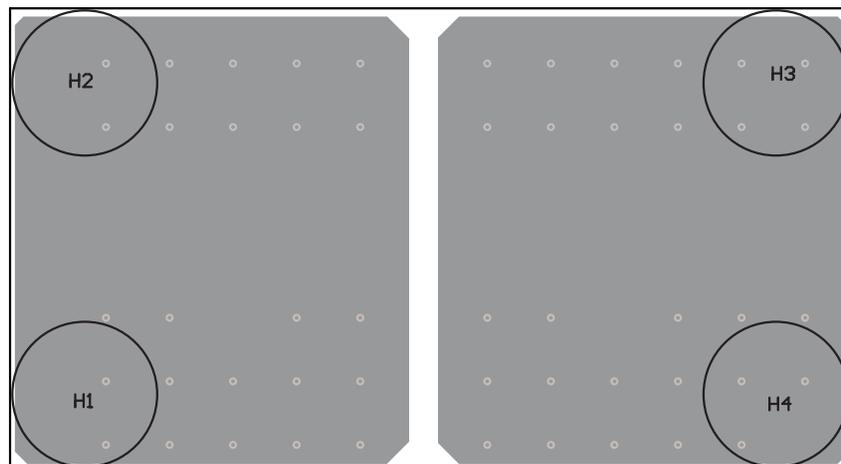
ISO6521REUEVM PCB 布局 - 复合底视图
